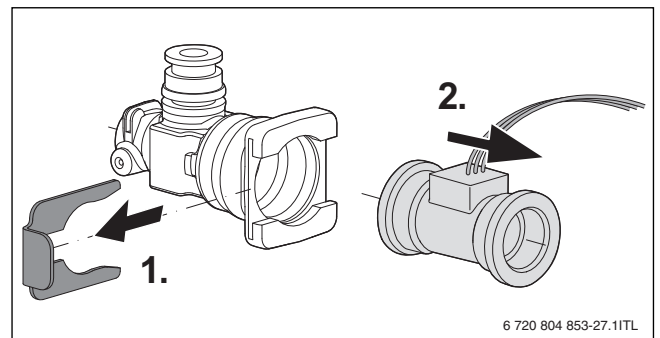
Smontaggio della turbina dal tubo dell'acqua fredda
